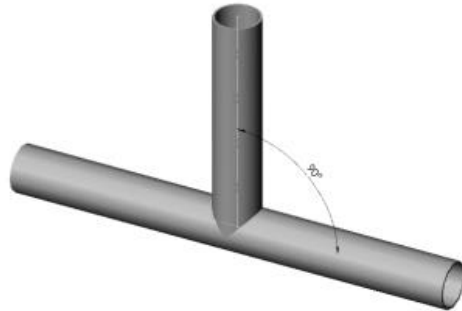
Chasis monocasco, Muestra de Soldadura 1. [1].
